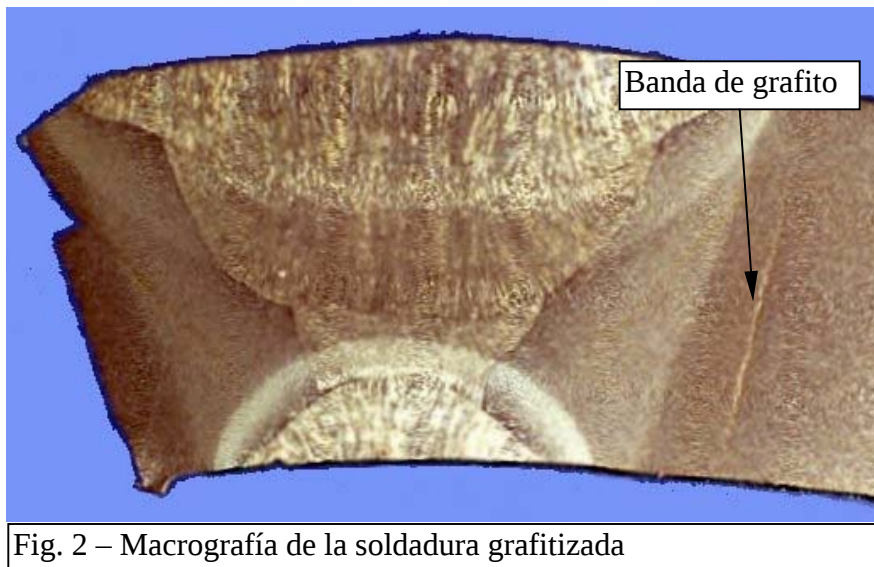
Macrografía de la soldadura grafitizada
